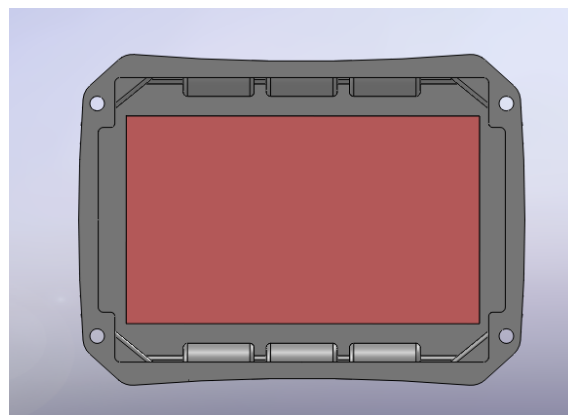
Innenkontur der Rückseite des Gehäusedesigns 2 mit eingelegtem Akku
